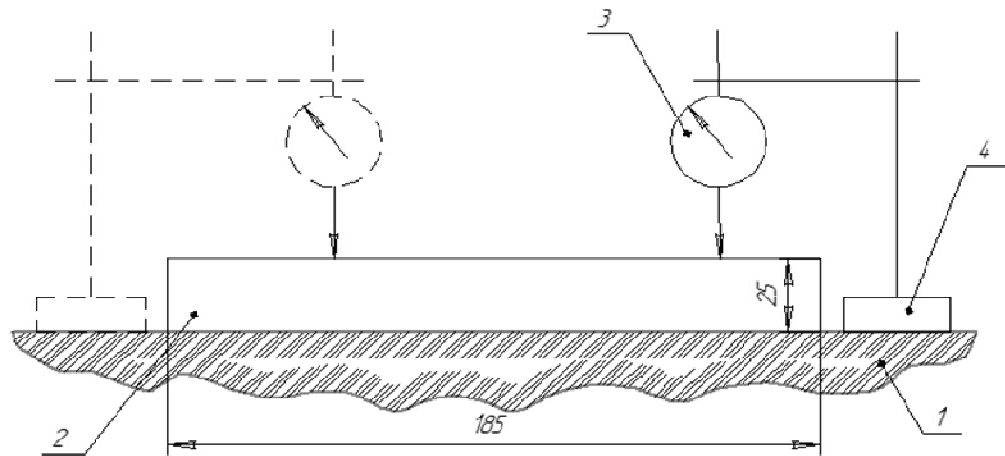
Контрольно-вимірювальний пристрій
